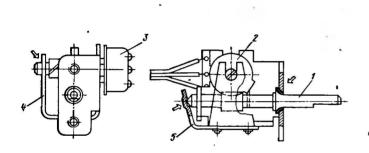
Механизма плавной настройки раднопрнемника автомагнитолы «Былина РМ-317СА»: I — вал ручки настройки; 2 — зубчатое колесо; 3 — резистор типа СПЗ-4аМ; 4 — скоба; 5 — пружина (Стрелкой ⇒ показаны места смазки механизма настройки
